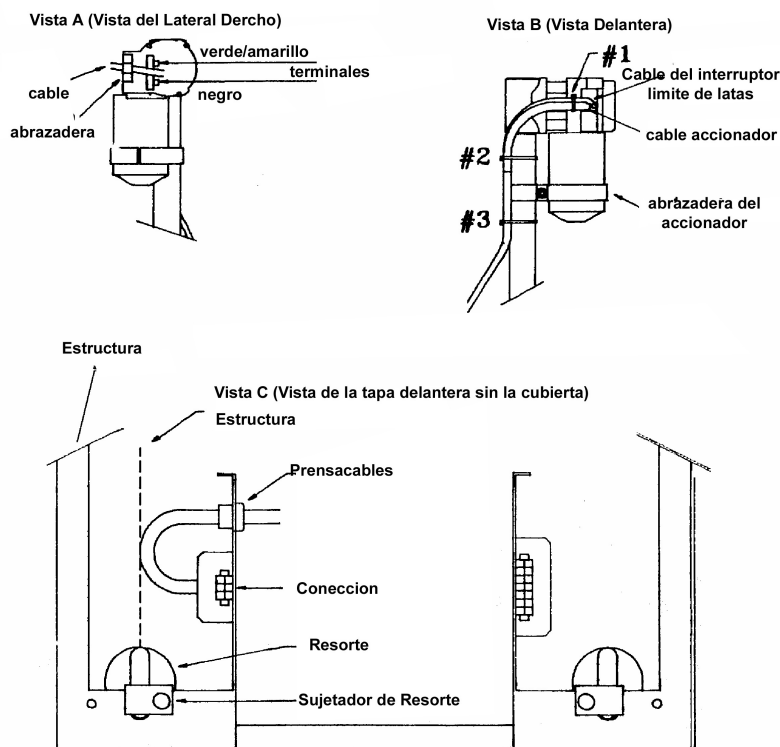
REEMPLAZO DEL CABLE DEL ACCIONADOR
